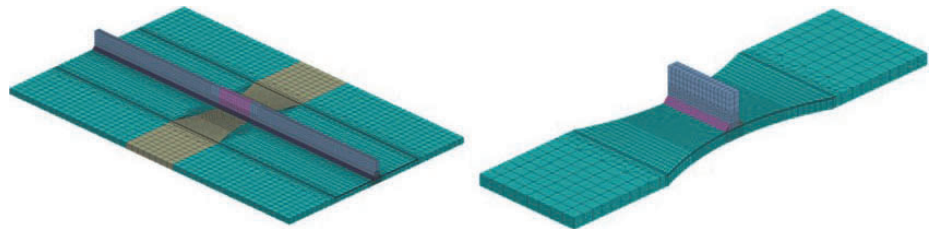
Grundplatte mit aufgeschweißter Quersteife (links) und einzelne Probe (rechts) [2]
